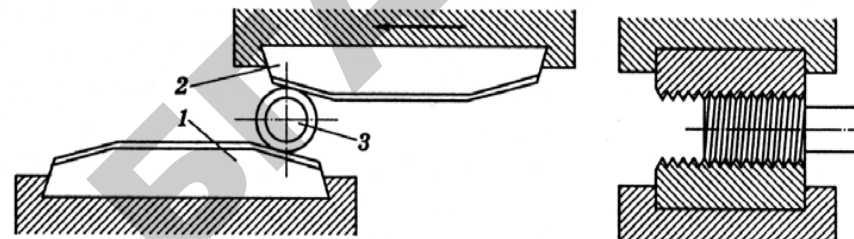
Схема накатывания наружной резьбы на накатном станке:
